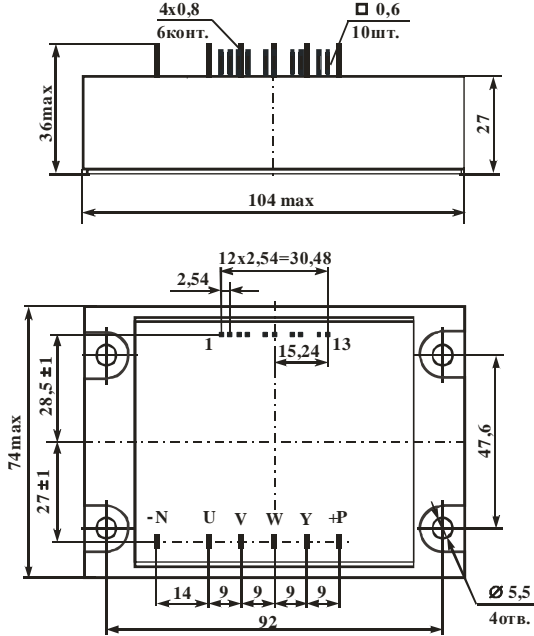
Габаритный чертеж модуля M13B-10-1
